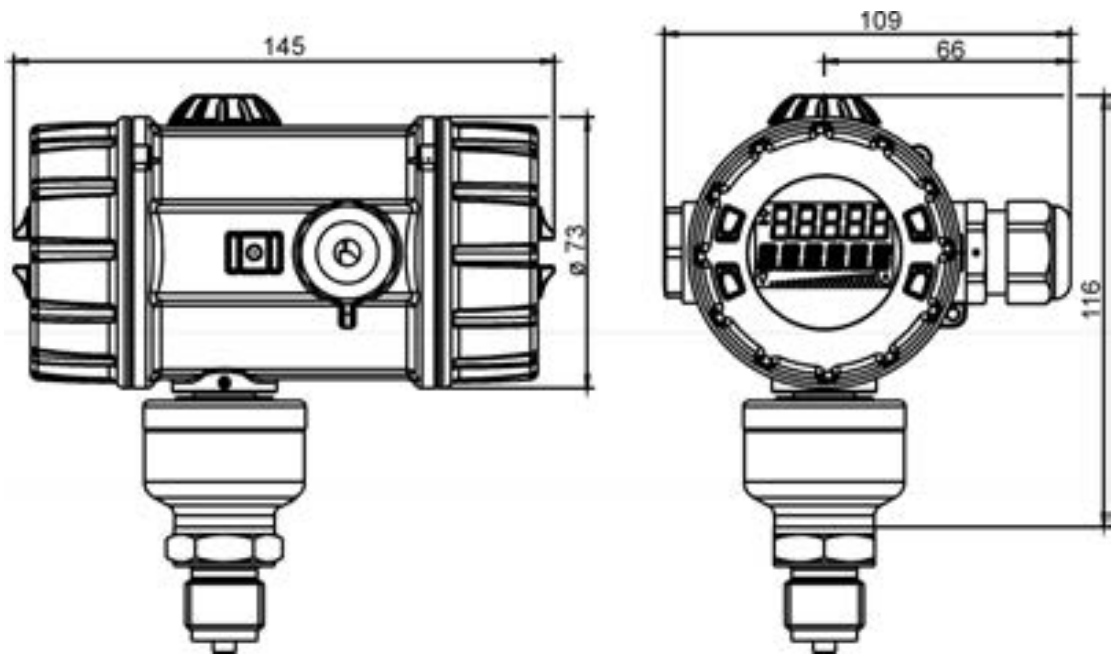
Габаритные размеры преобразователя давления Альбатрос р20 (длинный корпус, прецизионное литье, с металлическим кабельным вводом)
